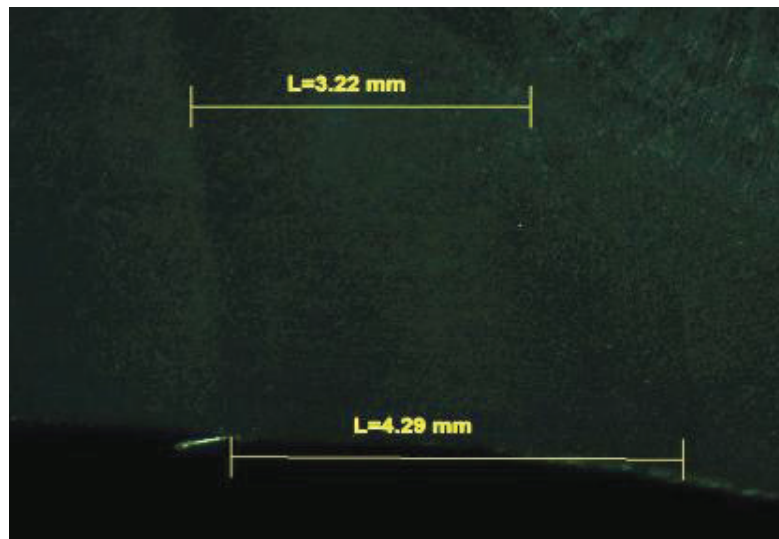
9 Macrografía del segundo pase de soldadura (caliente) realizado con proceso SMAW (6G), presenta buena penetración y fusión, 30X. Las dimensiones indican la longitud de la zona de soldadura y las zonas afectadas por el calor.
